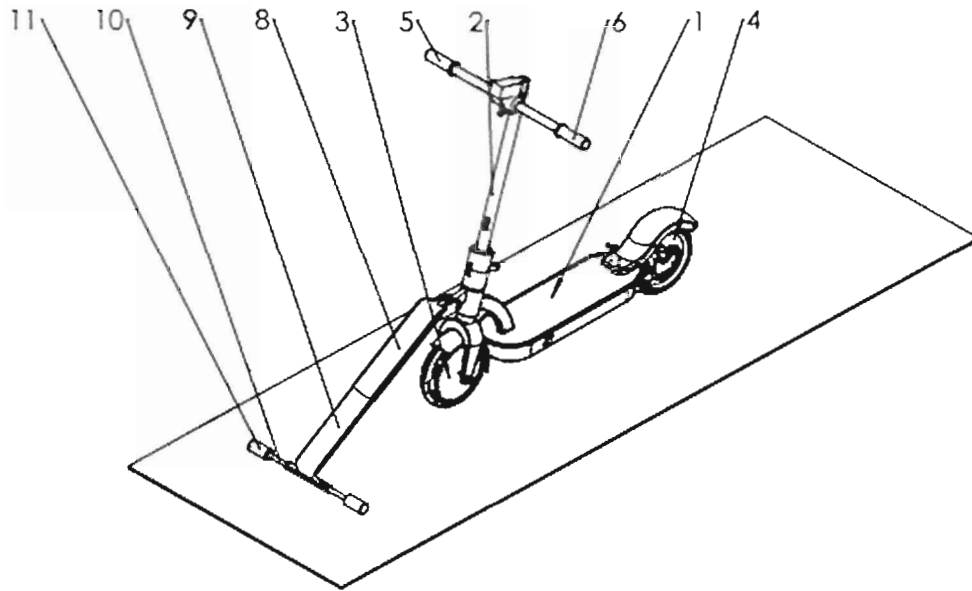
Troțineta electrică cu sistem anti-răsturnare tip braț rabatabil– varianta constructivă 2
